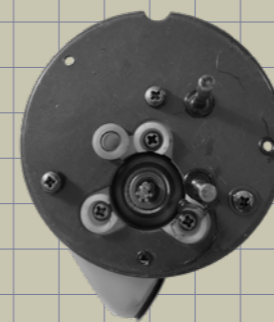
Vue du carter de protection moteur. L'axe cranté rotatif émerge de la bobine.
